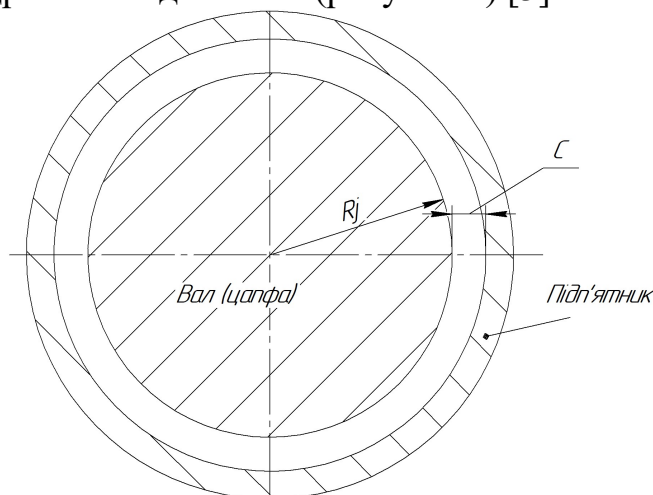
Схема гідродинамічного циліндричного підшипника ковзання
